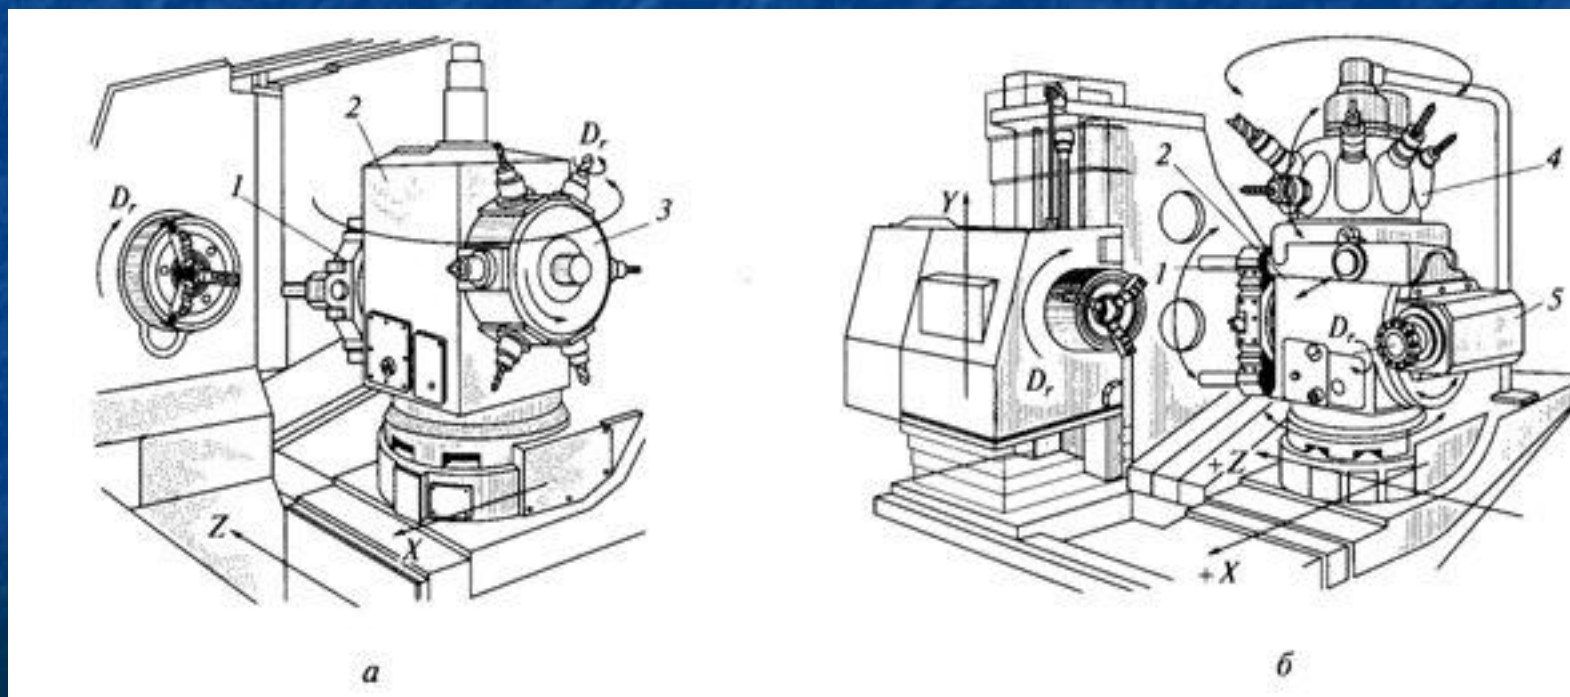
Горизонтальный многоцелевой сверлильно-фрезерно-расточный станок с ЧПУ:
